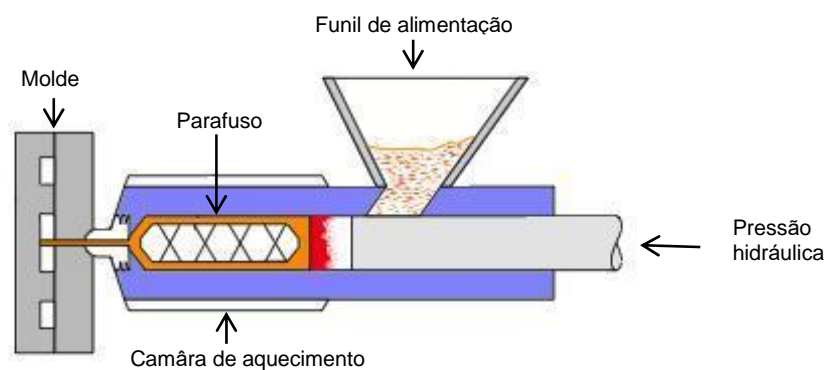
Secção de uma máquina de moldagem e injeção (Adaptado de Callister, 2007)
